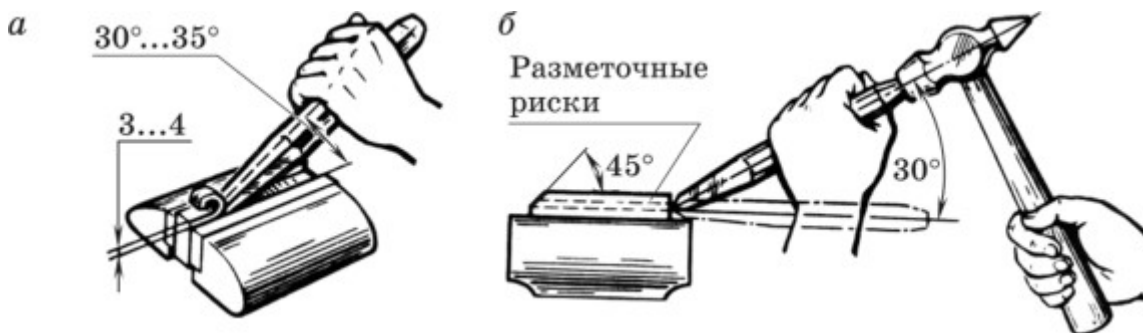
Рубка полосового и листового металла в тисках по разметке
